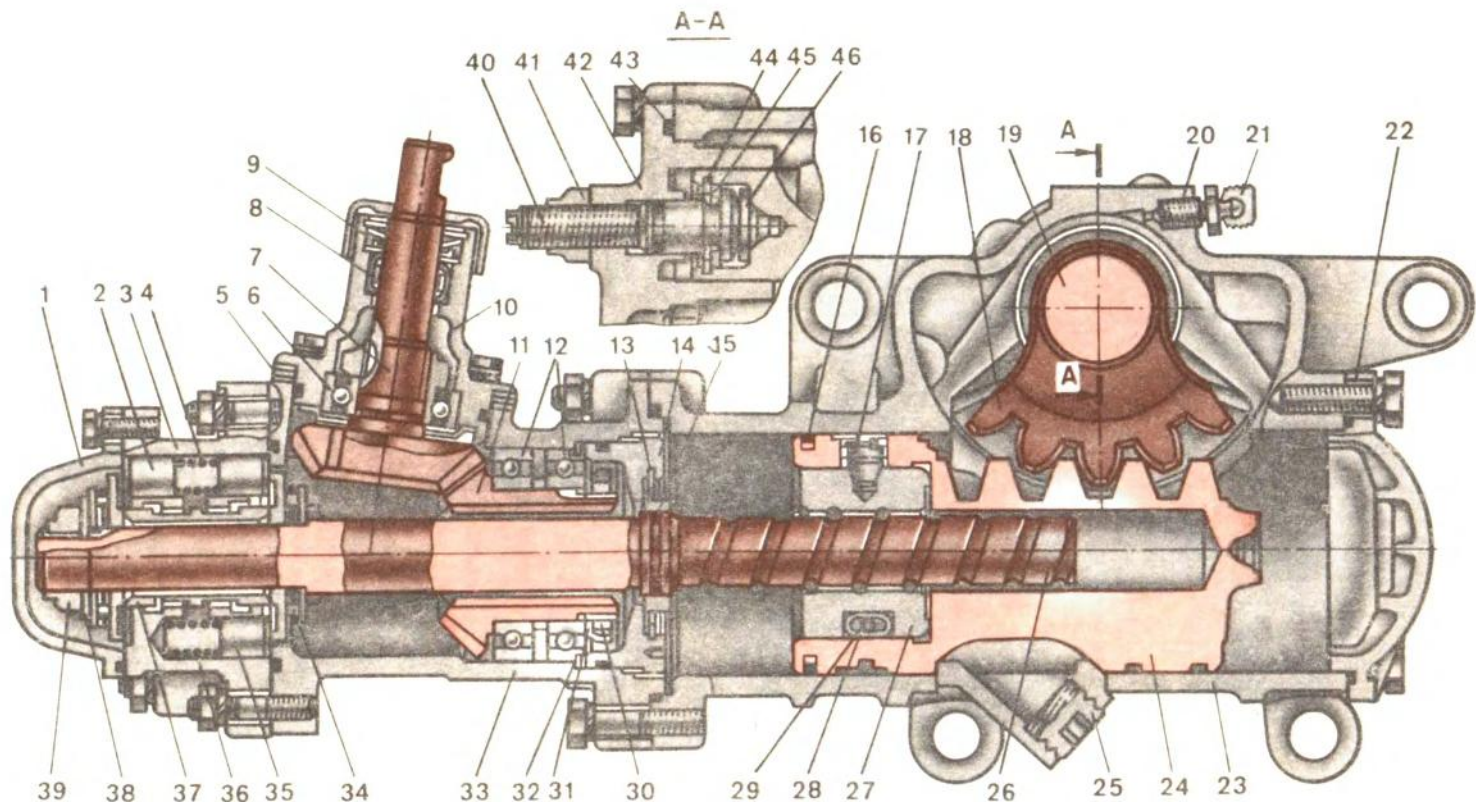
Рулевой механизм автомобиля КамАЗ-5320:
